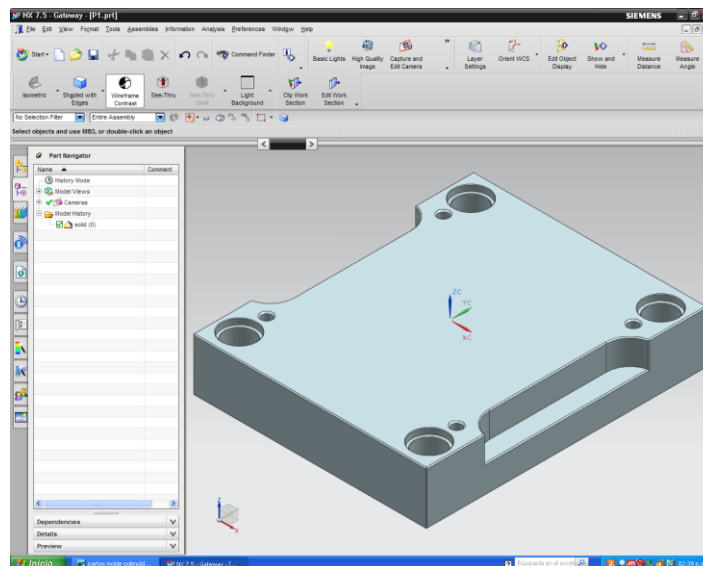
Placa frontal de cavidad P1, vista isométrica.
